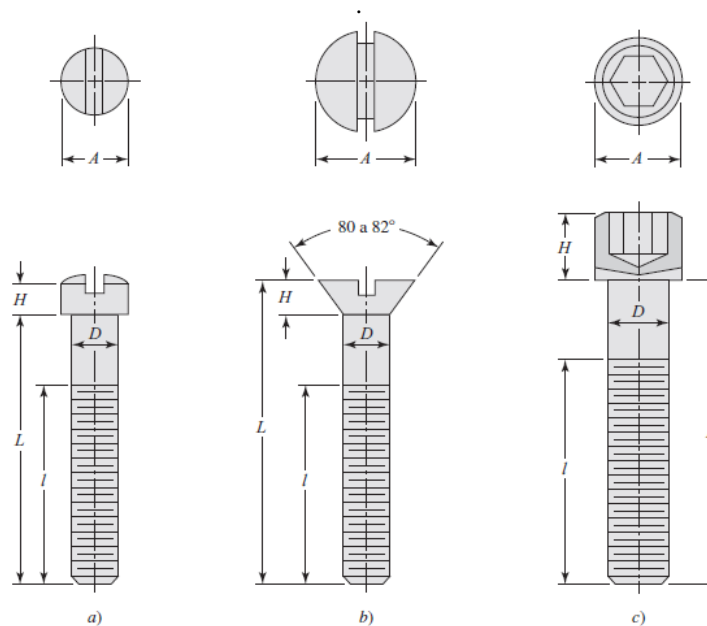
Cabezas usuales de tornillo: a) cilíndrica ranurada; b) plana; c) hueca hexagonal.
